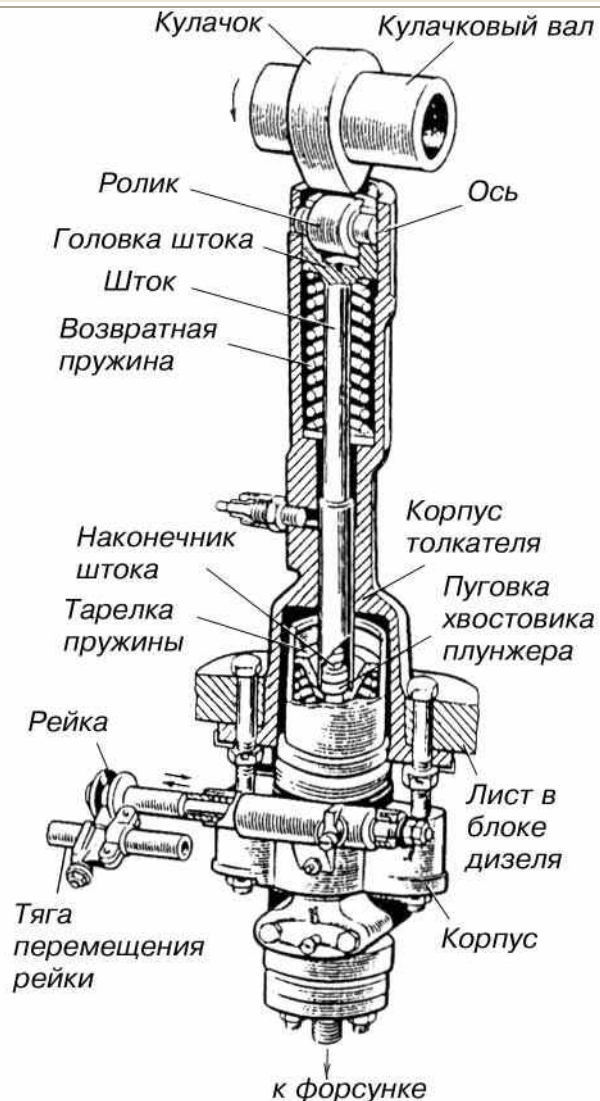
Толкатель и топливный насос дизелей 10Д100, 2Д100
